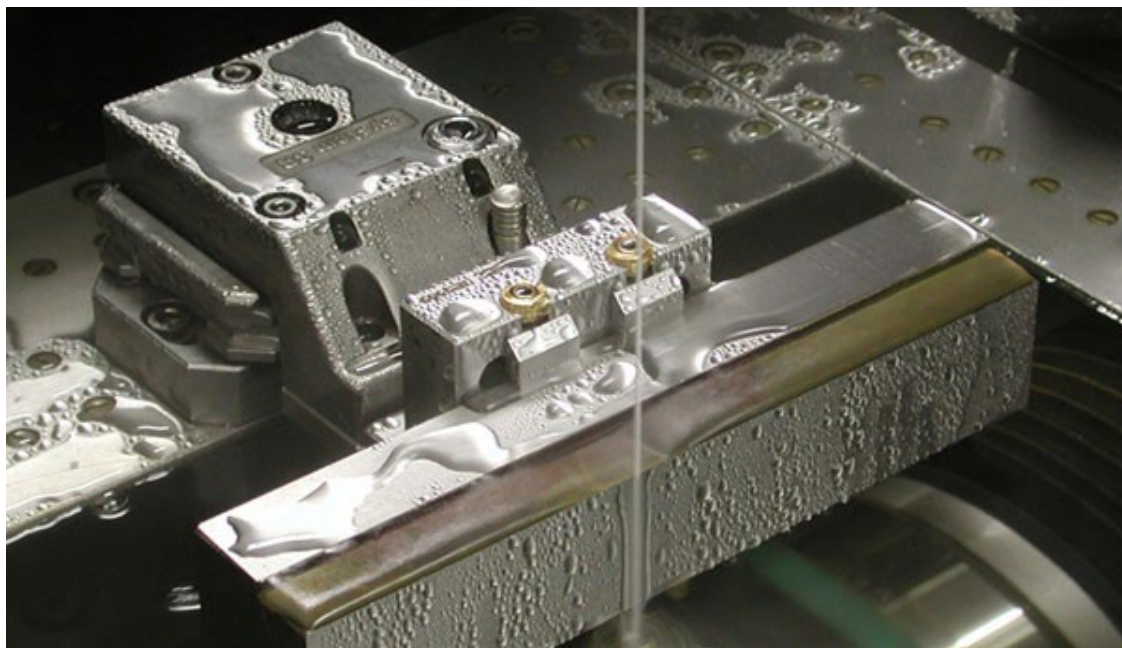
Базування допоміжної плити в лещатах
